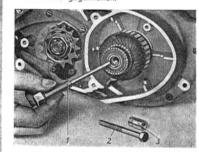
Abziehen des Lichtmaschinenankers mit Abdrück-schraube Nr. 0100027 (1). 2 = Ankerbefestigungsschraube, 3 = Unterbrechernocken
